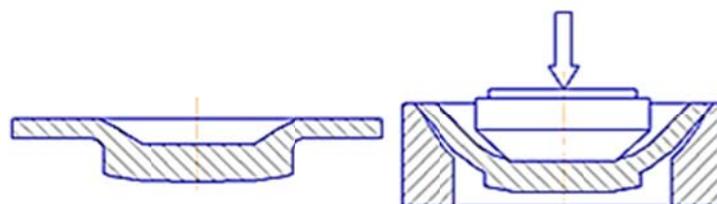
Схема получения поковки дна корпуса реактора, вытяжкой в штампе
